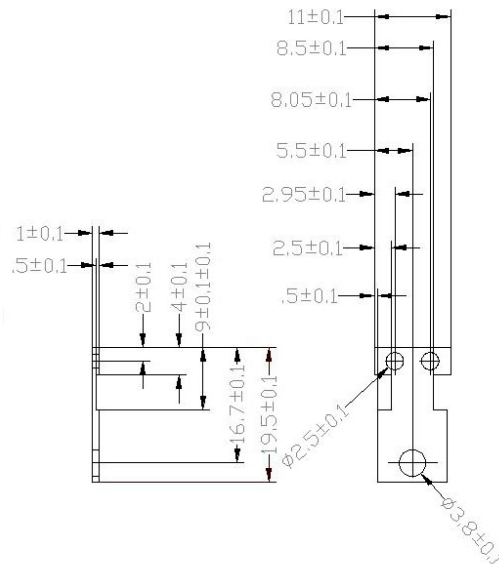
Dessin technique de la plaque aluminium pour les anneaux 4 et 6.
